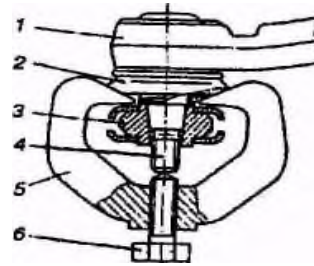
Выпрессовка пальца шарового шарнира из отверстия кронштейна стойки передней подвески автомобиля ЗАЗ-1102:
